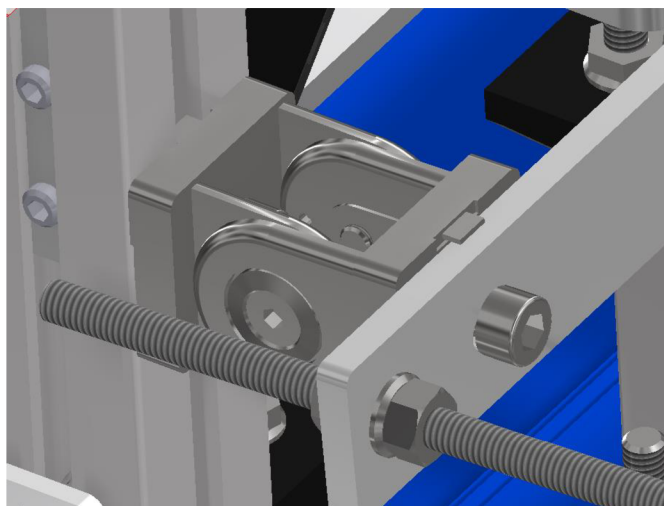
Detail přitlačné části horního rozpěrného mechanismu
